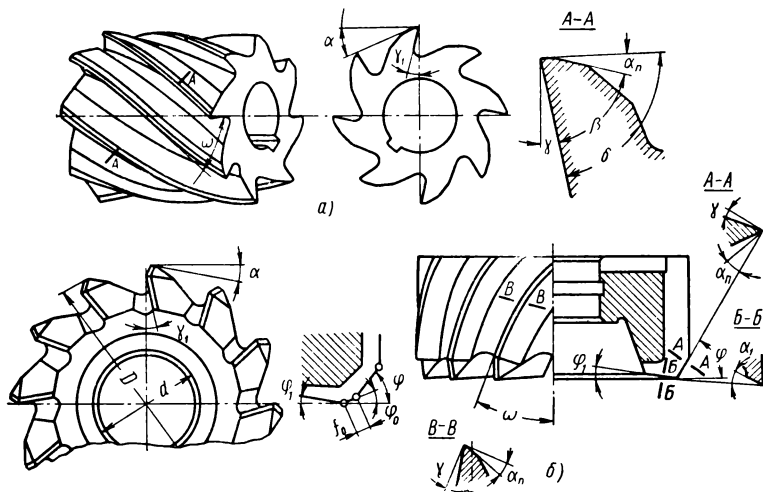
Геометрические параметры режущей части фрез из быстрорежущей стали:
